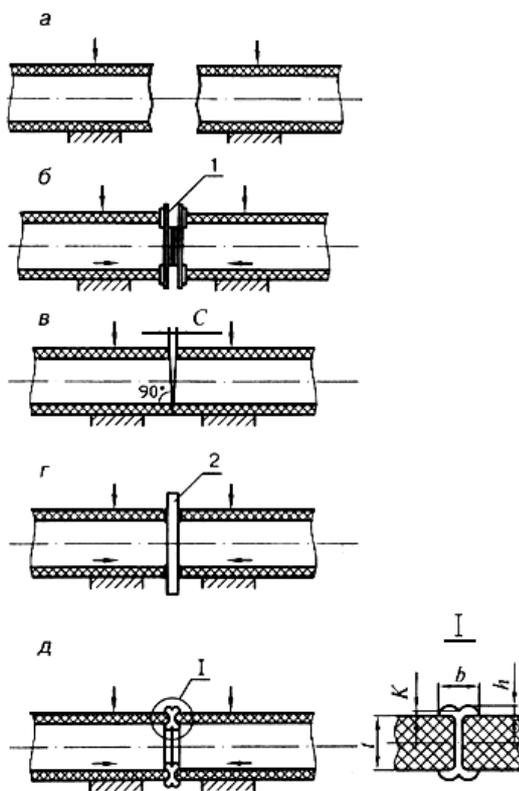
Последовательность процесса сборки и сварки встык труб из ПК: а - центровка и закрепление в зажимах сварочной машины концов свариваемых труб; б - механическая обработка торцов труб с помощью торцевателя 1; в - проверка соосности и точности совпадения торцов по величине зазора C ; г - оплавление и нагрев свариваемых поверхностей нагретым инструментом 2; д - осадка стыка до образования сварного соединения
